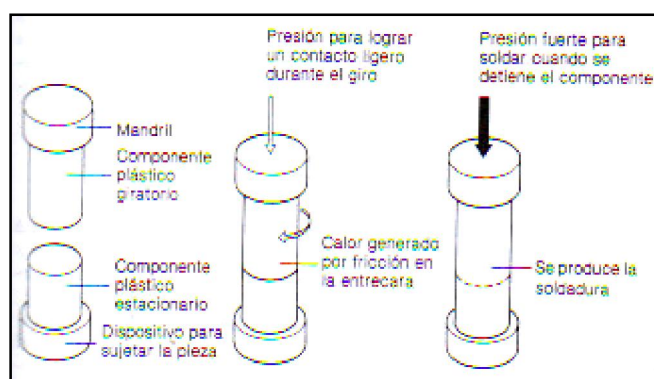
Procedimiento para la soldadura por fricción
